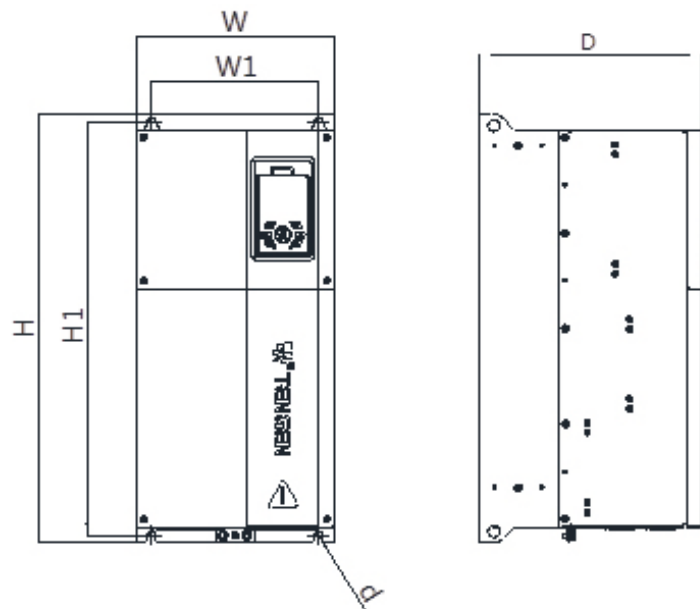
Габаритный чертеж типа F, типа G, типа H, типа I, типа J
